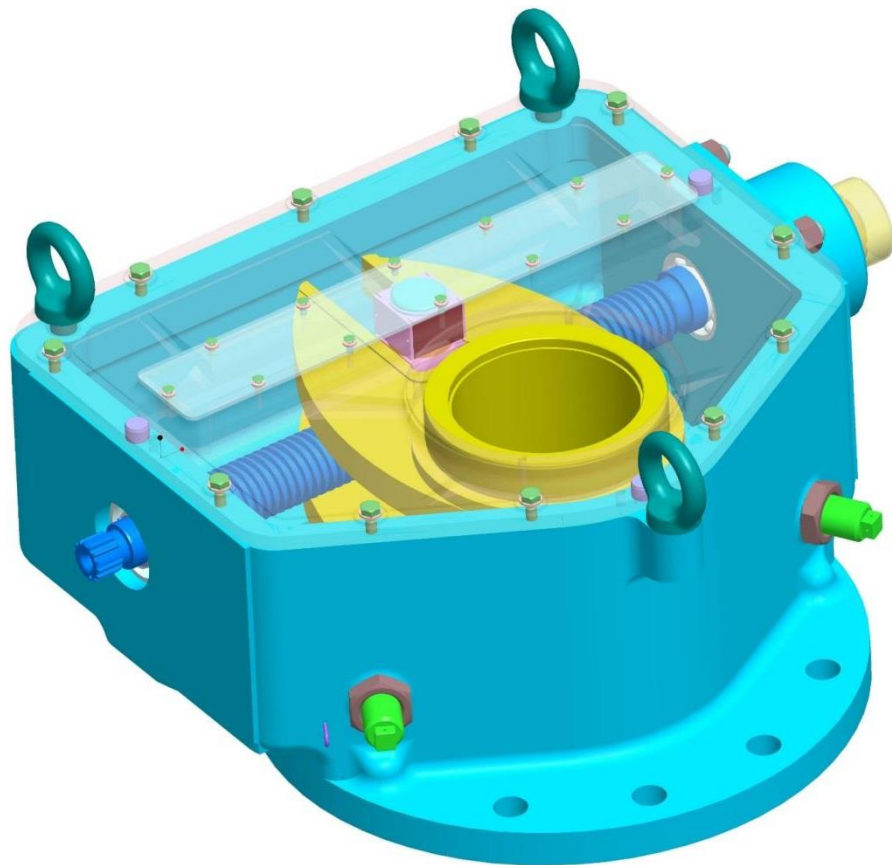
Загальний вигляд гвинтокулісного передаточного механізму
